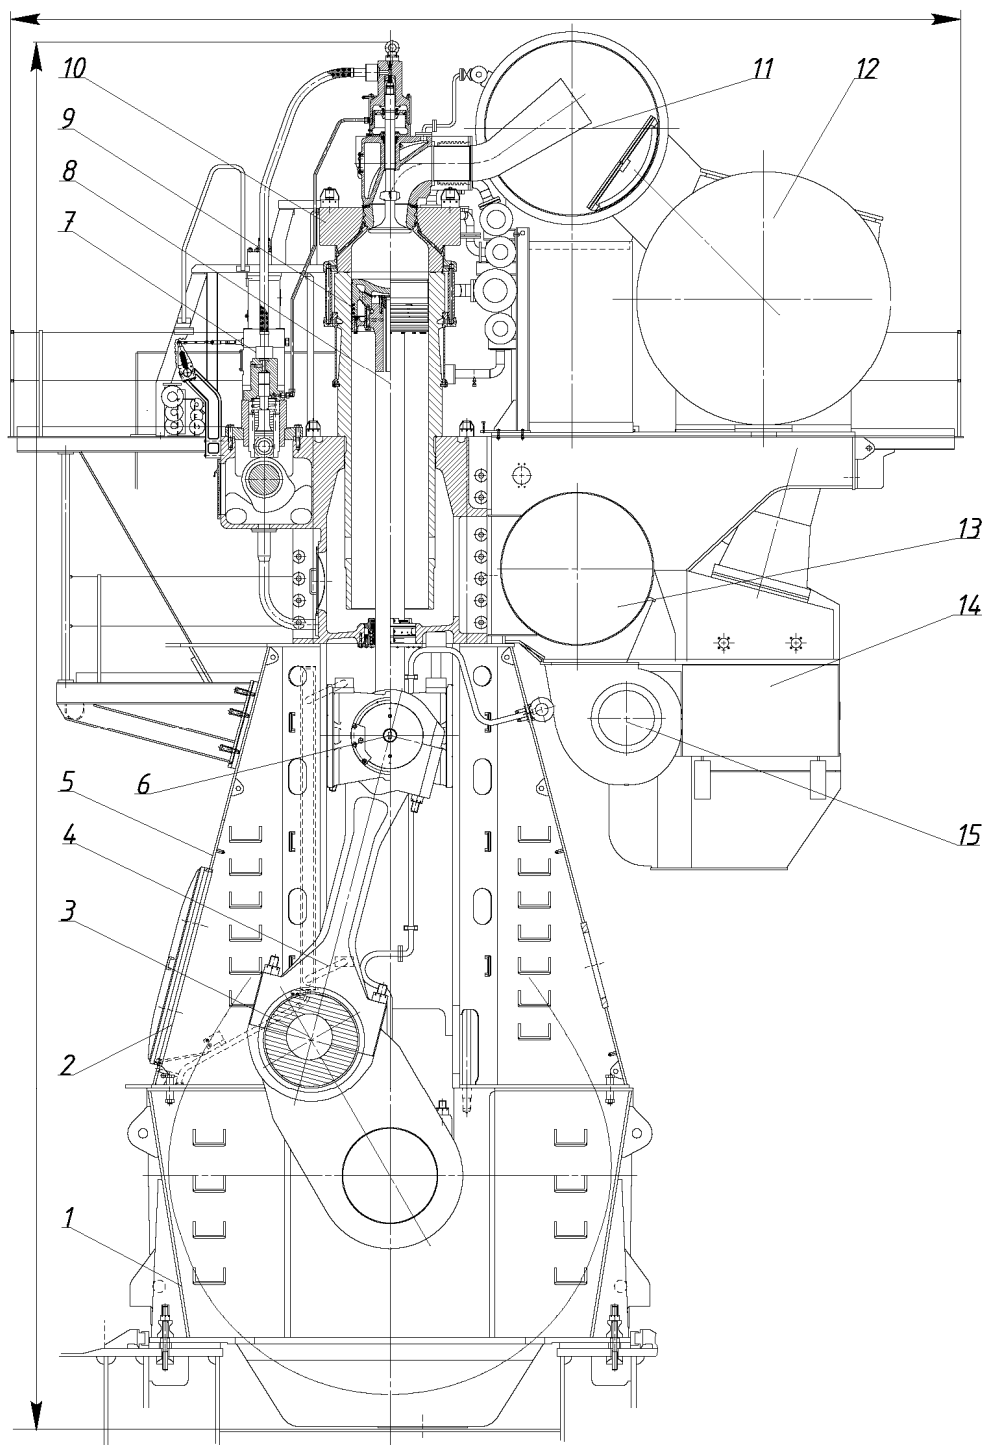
Головний дизель судна 7S70MC-C8 (поперечний перетин). 1 – фундаментна рама; 2 – люк картеру; 3 – колінчастий вал; 4 – шатун; 5 – коробка картеру; 6 – крейцкопф; 7 – блок насосів; 8 – шток поршня; 9 – поршень; 10 – кришка циліндра з клапаном; 11 – випускний ресивер; 12 – турбокомпресор; 13 – впускний ресивер; 14 – повітроохолоджувач; 15 – електроповітрорудувка
